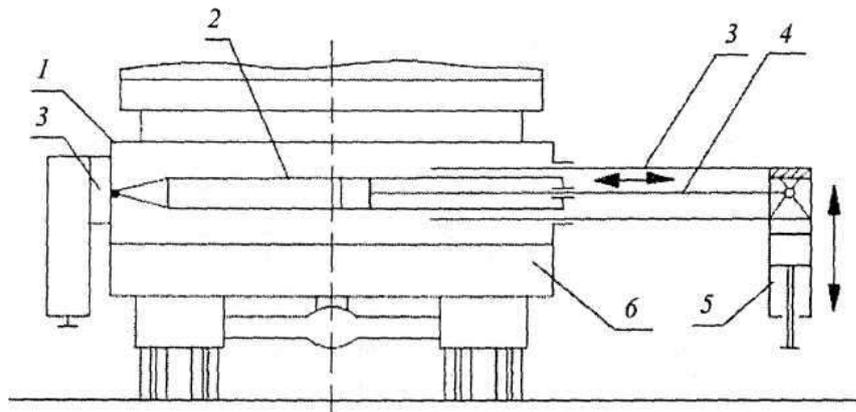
Опорное основание: 1 - балка наружная; 2 - гидроцилиндр выдвигания; 3 - балка внутренняя; 4 - шток; 5 - гидроцилиндр опоры; 6 – шасси
